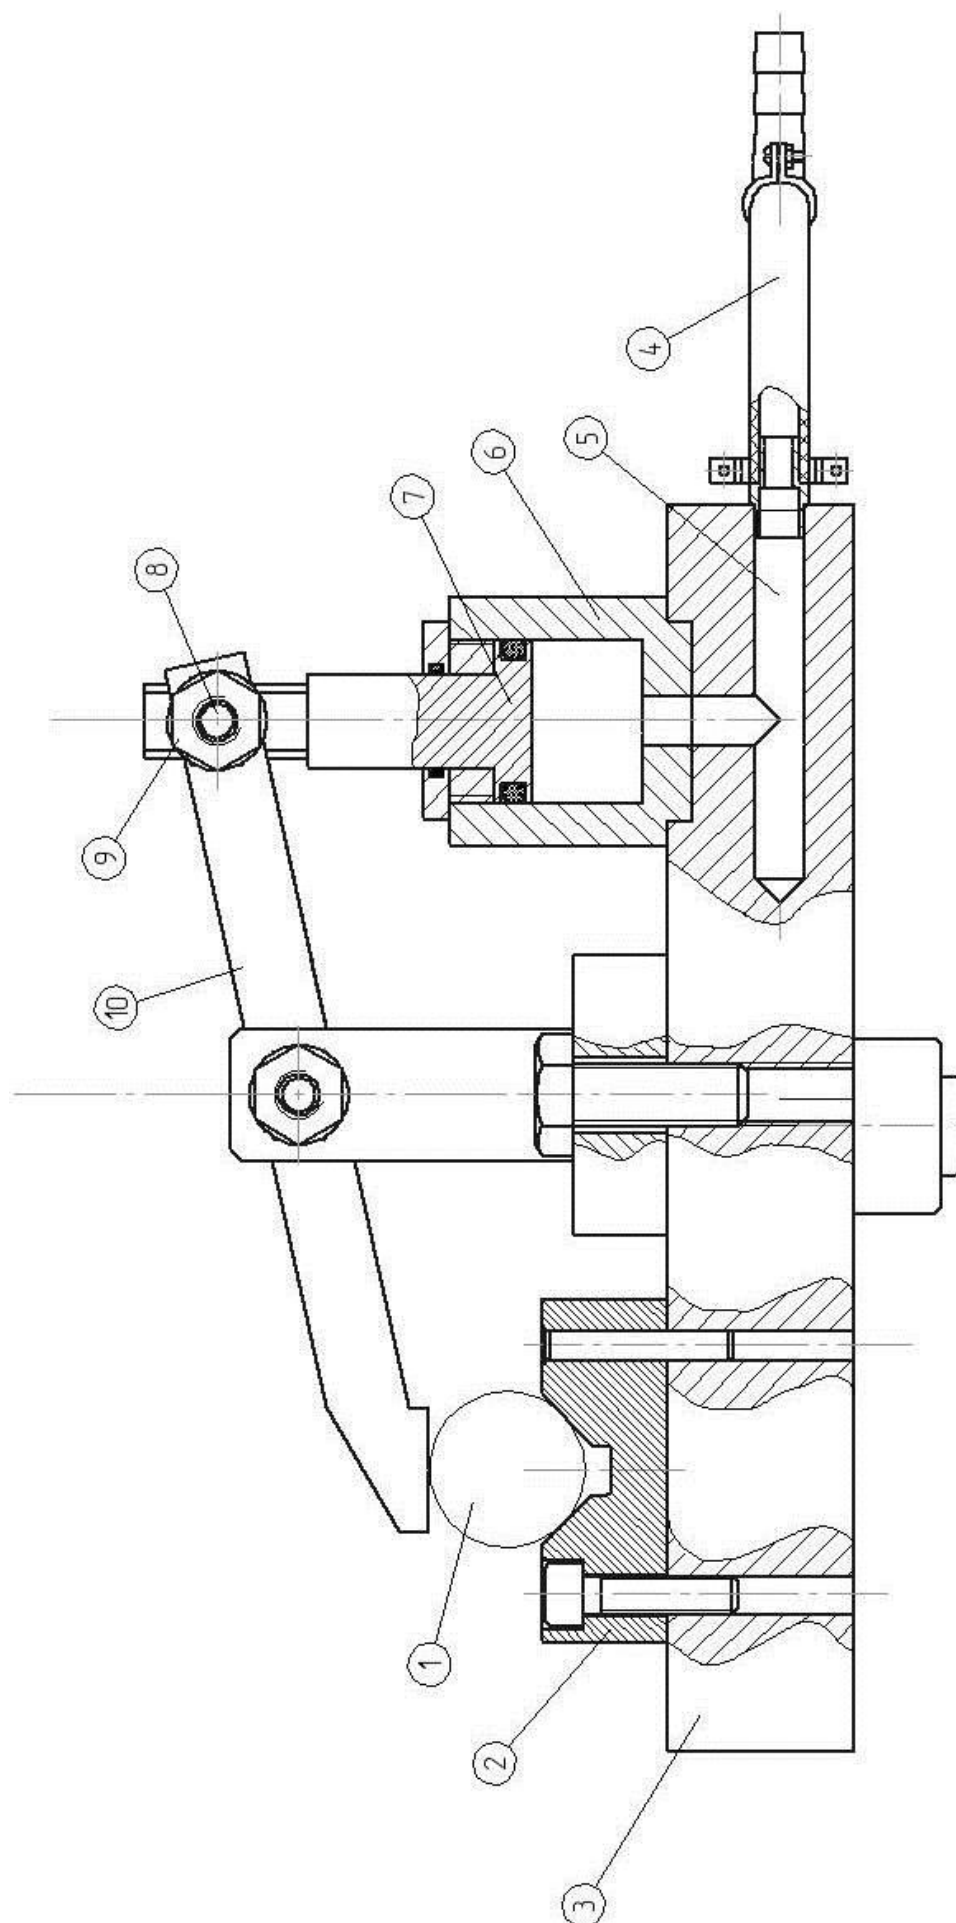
Чертеж приспособления для фрезерования шпоночных пазов на валу.
